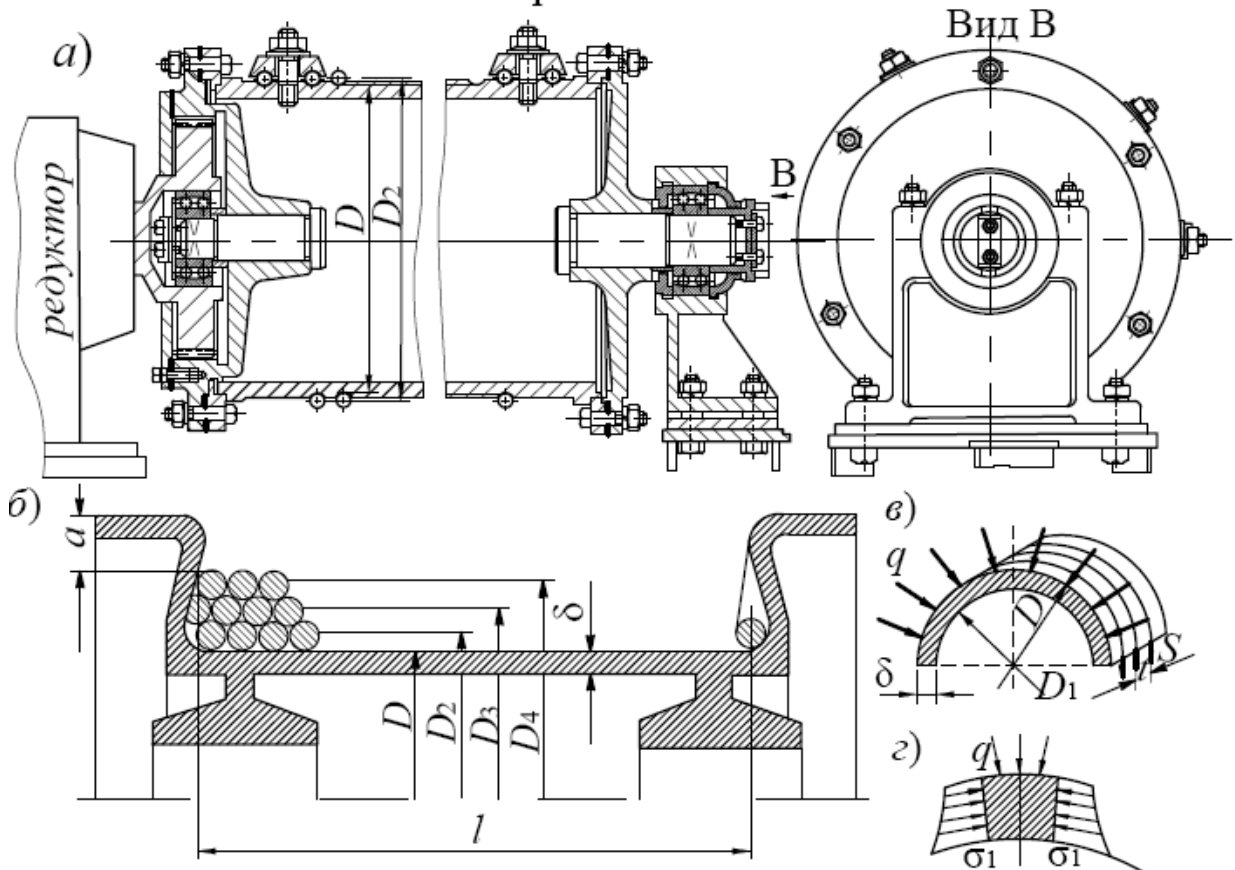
Грузовые барабаны: а – нарезной; б – гладкий; в – схема приложения сил сжатия; г – распределение напряжения сжатия в стенке барабана
